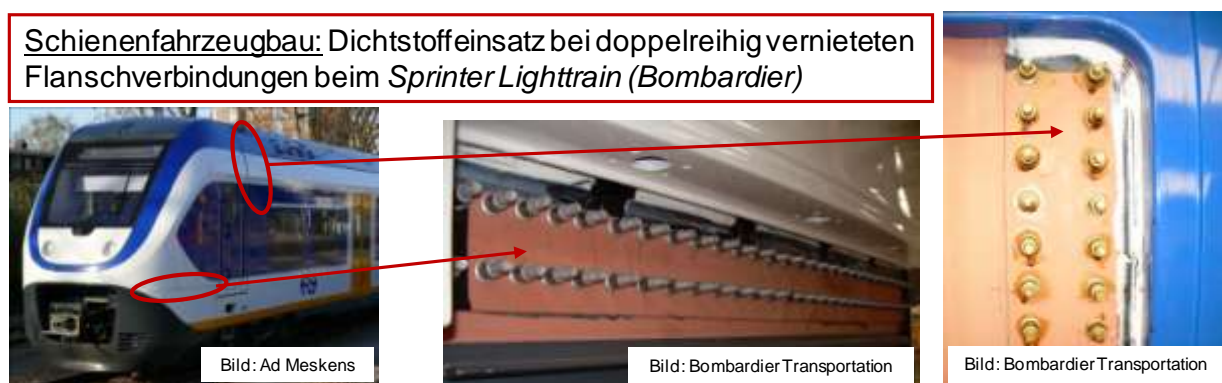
Einsatzmöglichkeiten tragfähiger und dichter Flanschverbindungen im Schienenfahrzeugbau
